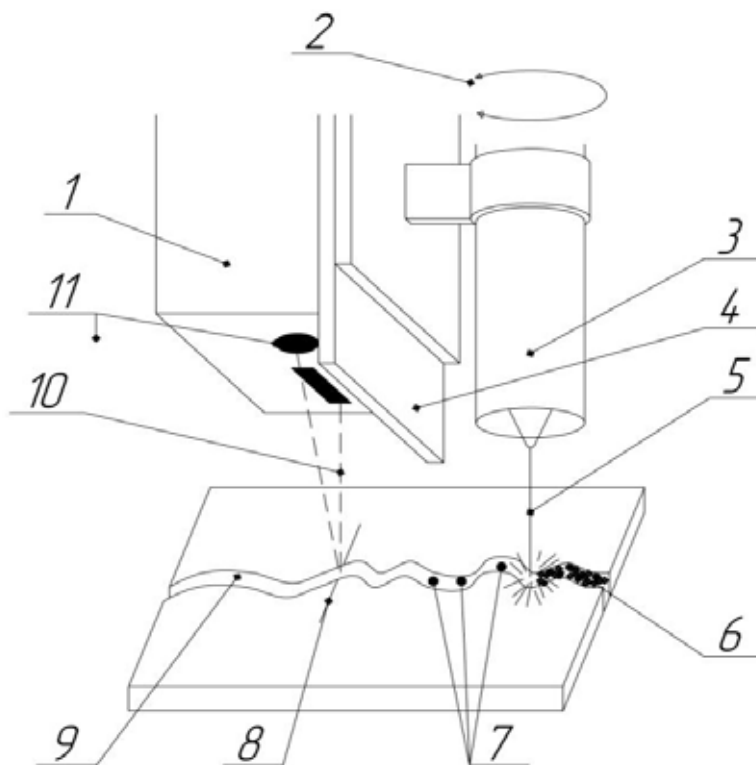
Схема работы системы: 1 — сенсор; 2 — вращение в запястье робота; 3 — сварочная головка; 4 — защитный экран; 5 — сварочная проволока 6 — сварочный шов; 7 — позиция коррекции; 8 — линия сканирования 9 — стык свариваемых деталей; 10 — сканирующий луч; 11 — камера [4]
